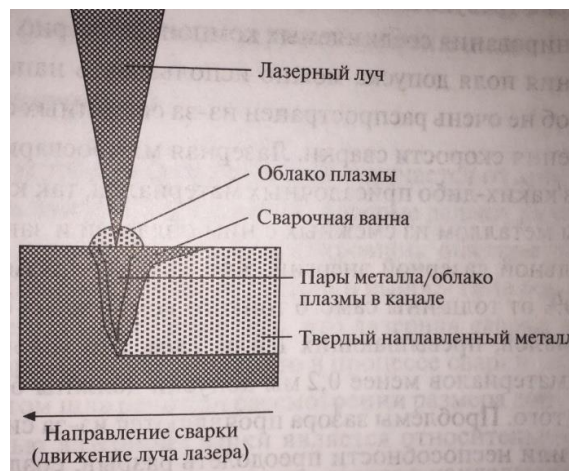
Основы лазерной сварки в режиме канала или глубокого проплавления
